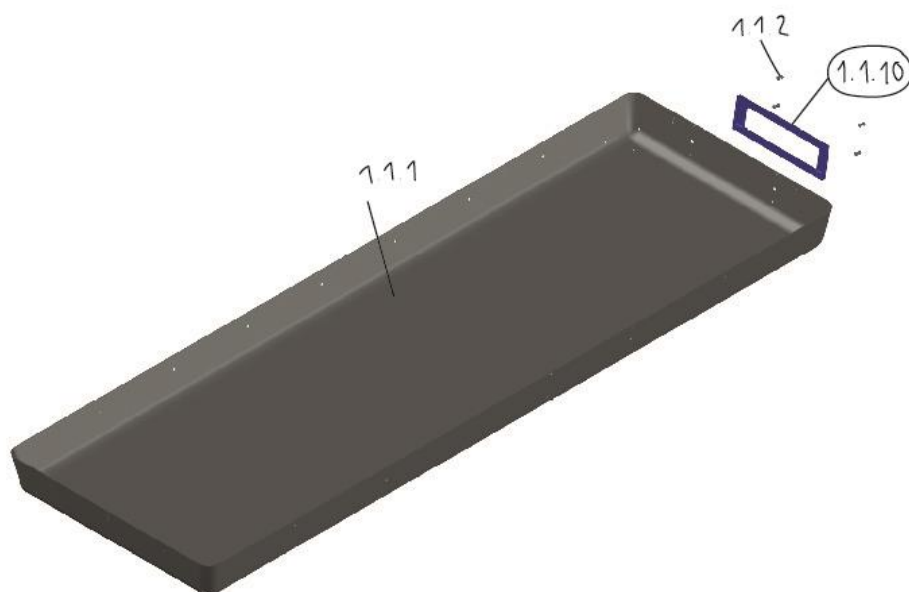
Explosionado de relaciones pieza 1.1.10
